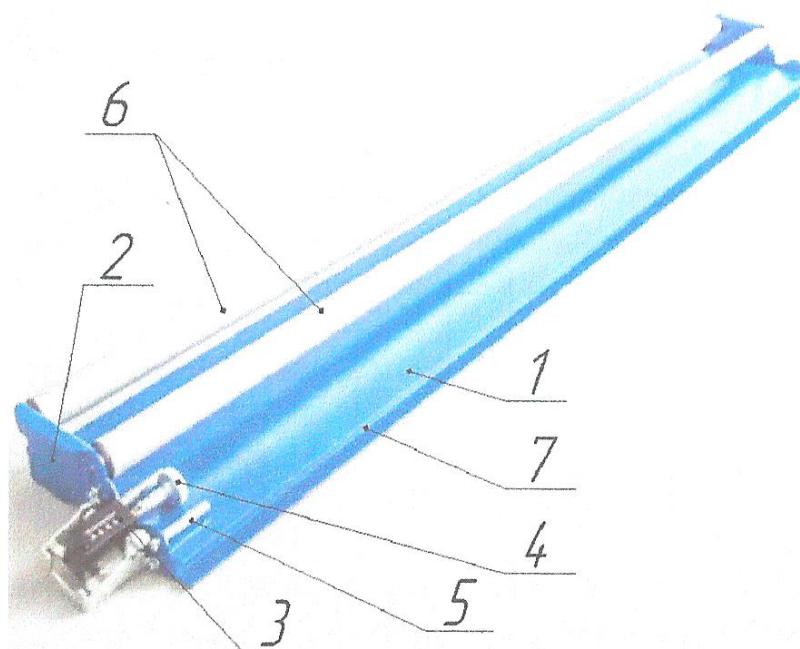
Устройство для перемотки пленки «Roll 1600» (1 - Основание-станина; 2 – Боковая стенка; 3 - Счетчик; 4 – Мерное колесо счетчика; 5 – Направляющий палец; 6 - Ролики; 7 – Упор для реза материала).
